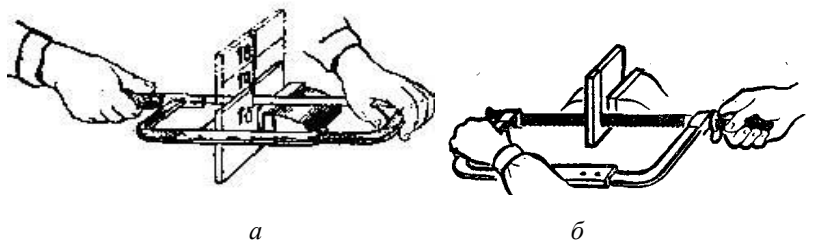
Приемы резания металла ручной слесарной ножовкой:
